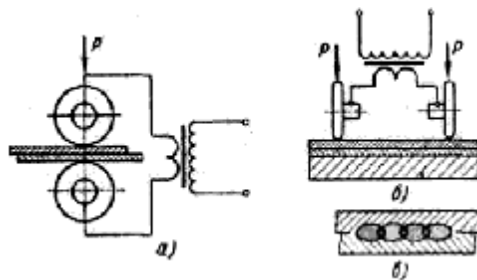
Схема процесса роликовой сварки (P — давление):
